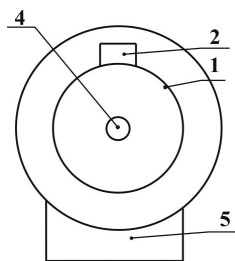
Двухчастотный вибровозбудитель, совмещенный с электродвигателем: 1 – корпус АБ; 2 – дебаланс; 4 – вал; 5 – электродвигатель
